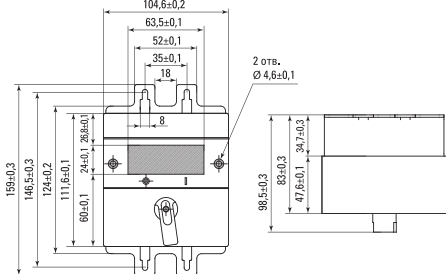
Габаритные размеры моторного привода к ВА-99М 250
